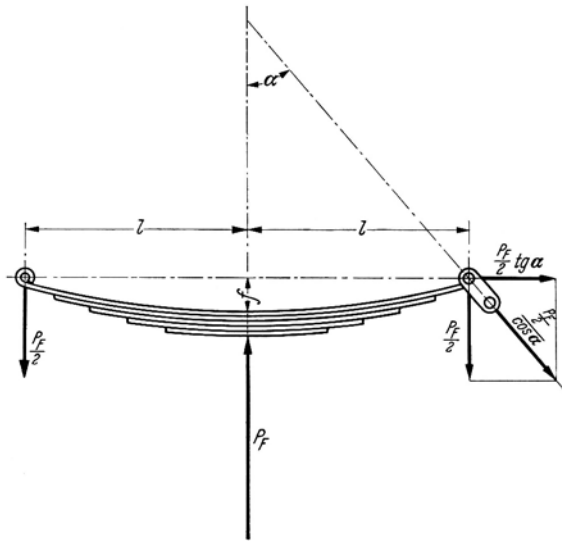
Beanspruchungen einer mittels Lasche aufgehängten Blattfeder.
